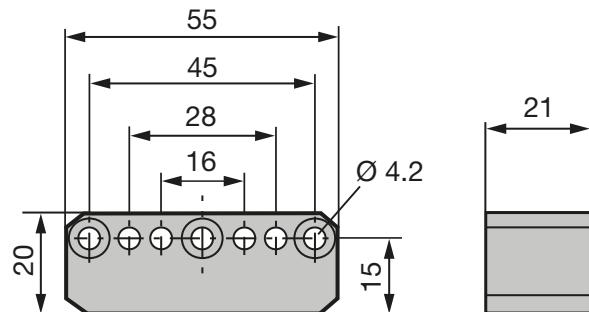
Medidas de montaje del sensor de posición BTL5-P-5500-2
